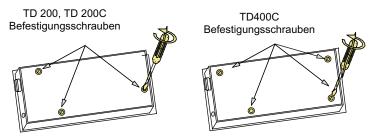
Entfernen der Befestigungsschrauben des Text Displays
